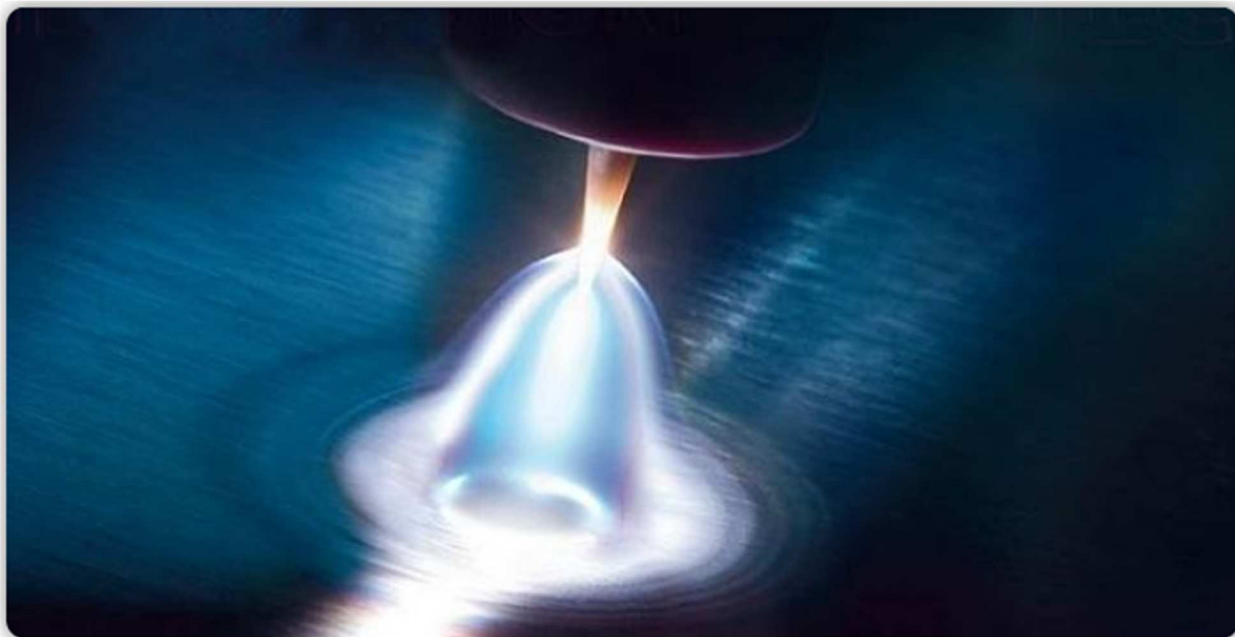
Процес зварювання аргоно-дуговим зварюванням зблизка
